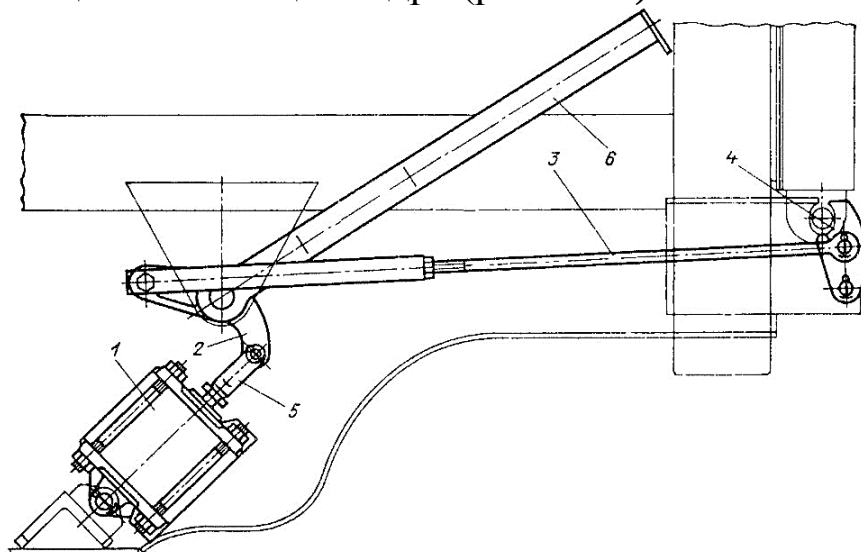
Пневматический привод управления запорами заднего борта: 1 – пневмоцилиндр; 2 – рычаг; 3 – тяга; 4 – запор борта; 5 – шток; 6 – рукоятка ручного открывания борта
